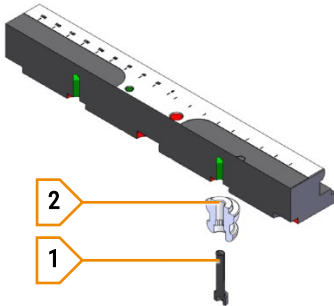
TeleCentric 125 – Befestigung mit NPSS
